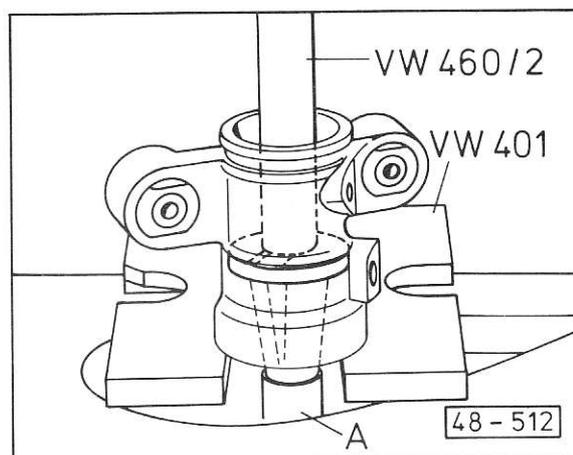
Bague-joint avec bague de roulement: extraction du boîtier
